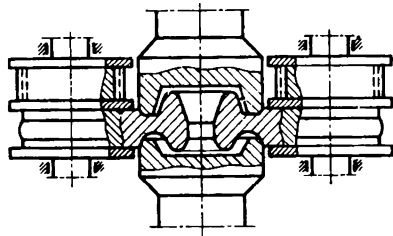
Схема накатки шестерни с радиальной подачей валков
